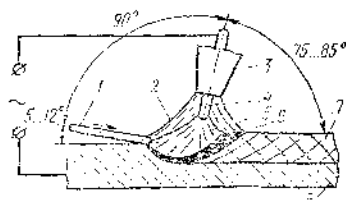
Схема ручной аргонно-дуговой сварки с присадочным прутом
